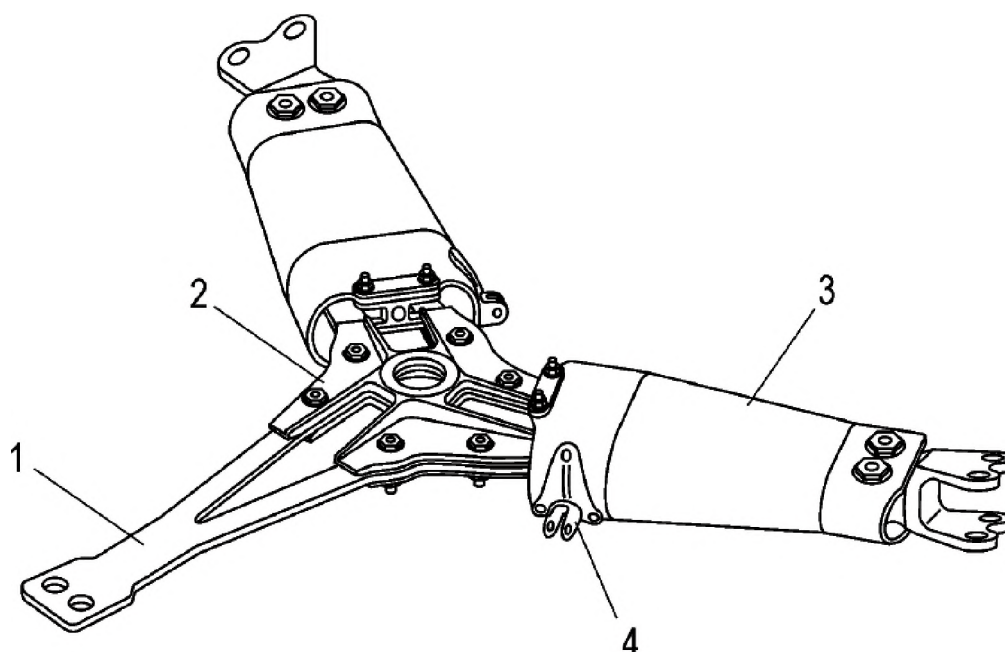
Схема втулки с пластинчатым V-образным торсионом: 1 – пластинчатый V-образный торсион; 2 – корпус втулки; 3 – кожух; 4 – рычаг поворота лопасти.
